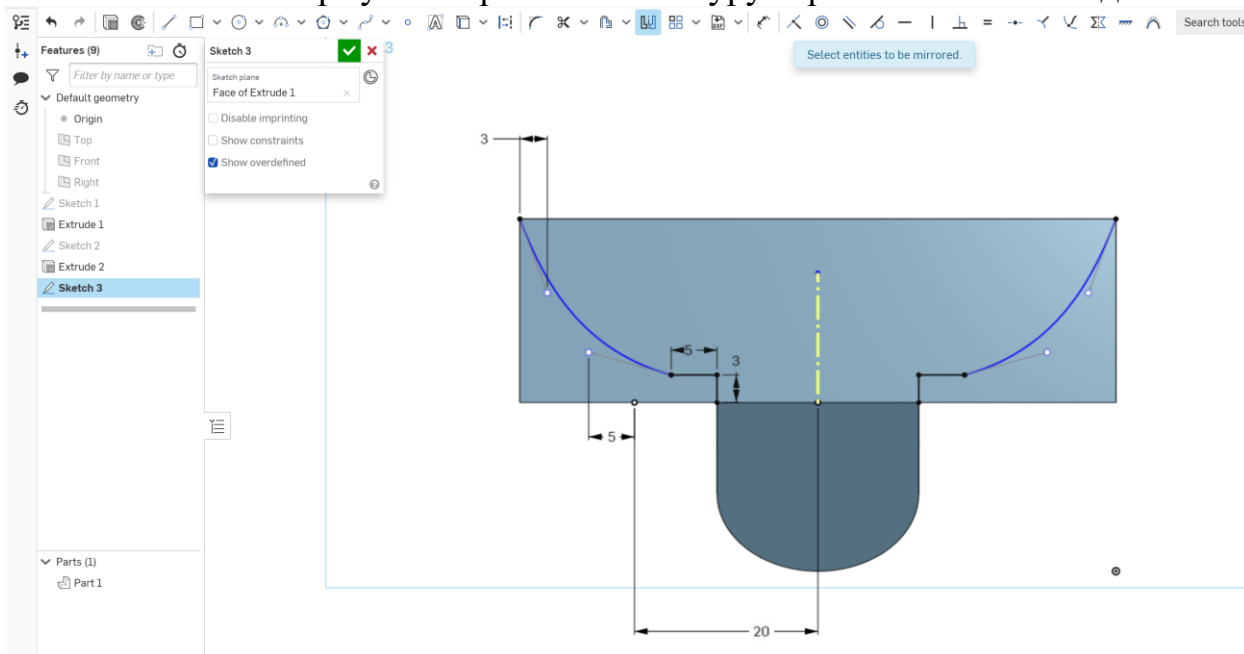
Формування робочого контуру верхньої частини з двох боків
